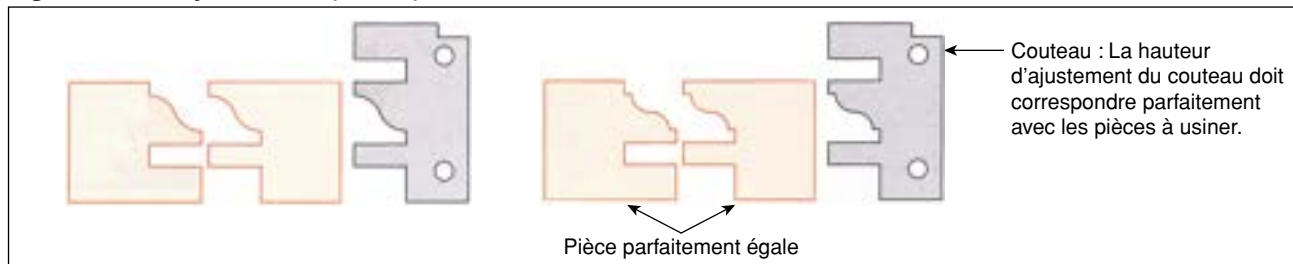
Outils de coupe pour profil et contre-profil (Dimar)
